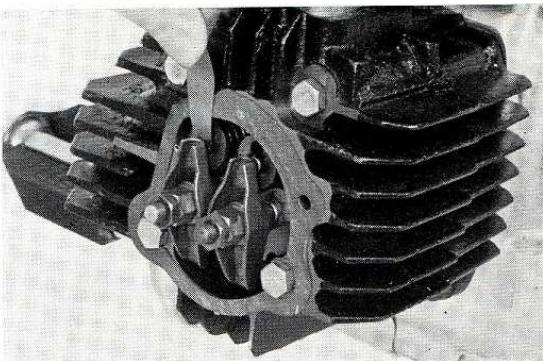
REGIAGE DES POUSSOIRS REGLAGE ET LA TIGE DE SOUPAPE.
